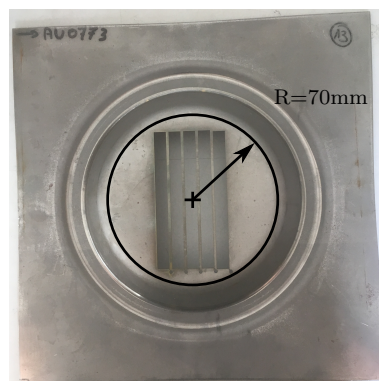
Extraction des éprouvettes d'Auto-Échauffement sur les gamelles après emboutissage
